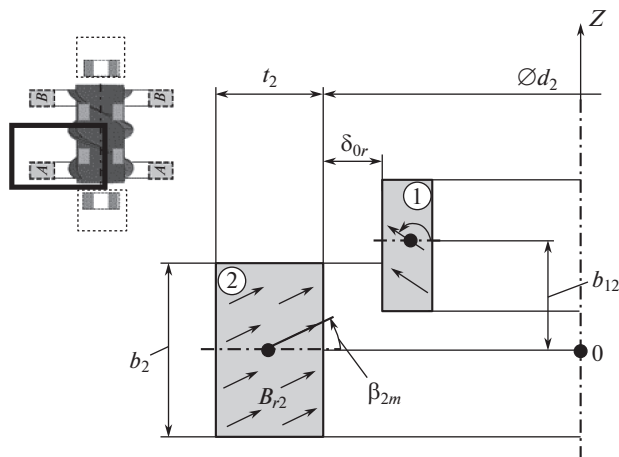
Характерные размеры пассивного магнитного подшипника.
